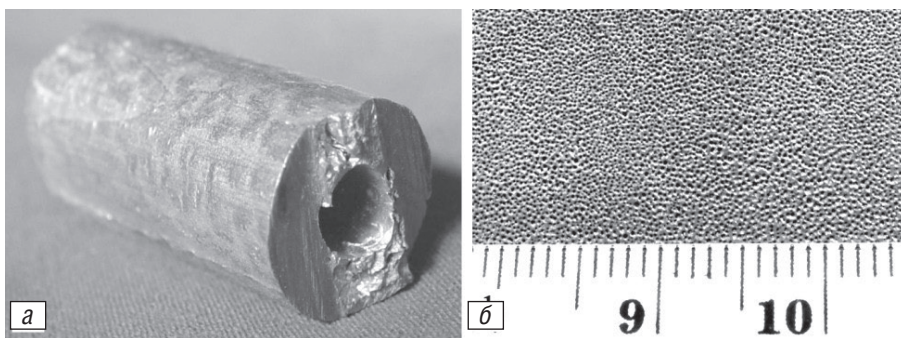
Различный диаметр пор в газарах: одна пора (\varnothing 13 мм) в цилиндрической отливке (а); газар с \varnothing пор 25 мк (б)
